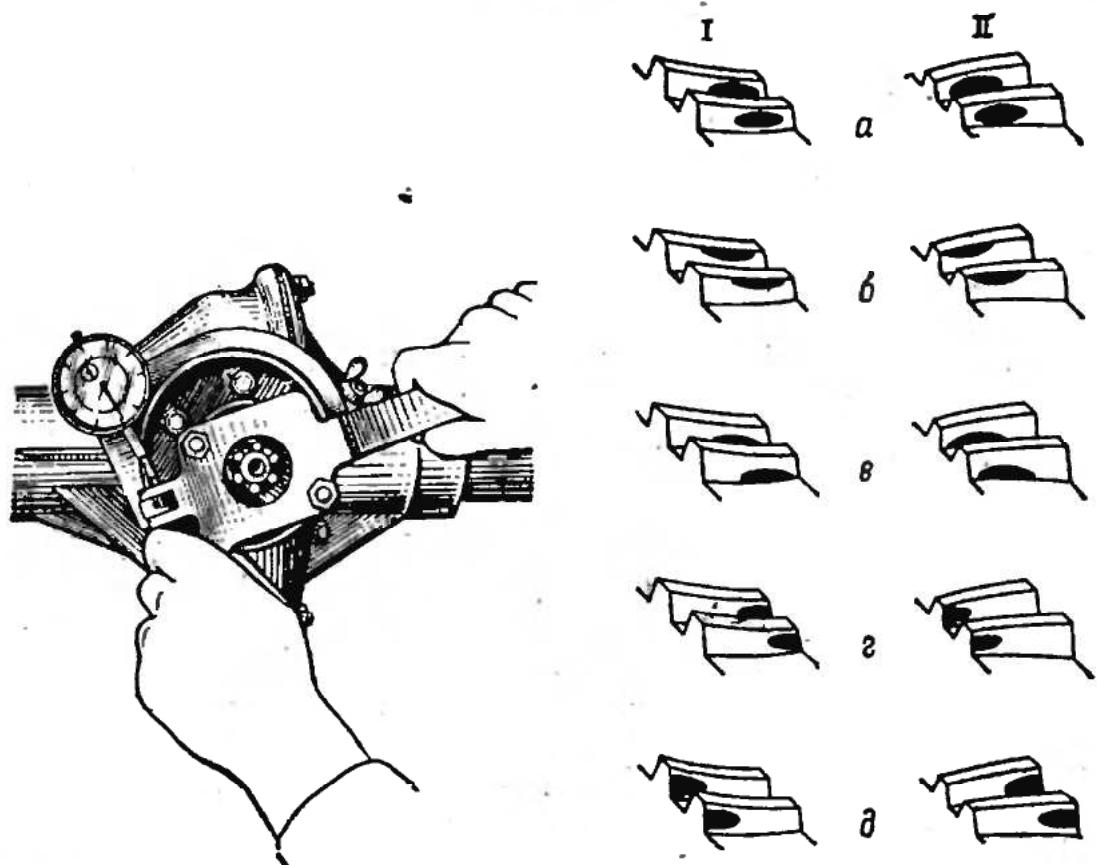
Проверка бокового зазора в зацеплении шестерен главной передачи
